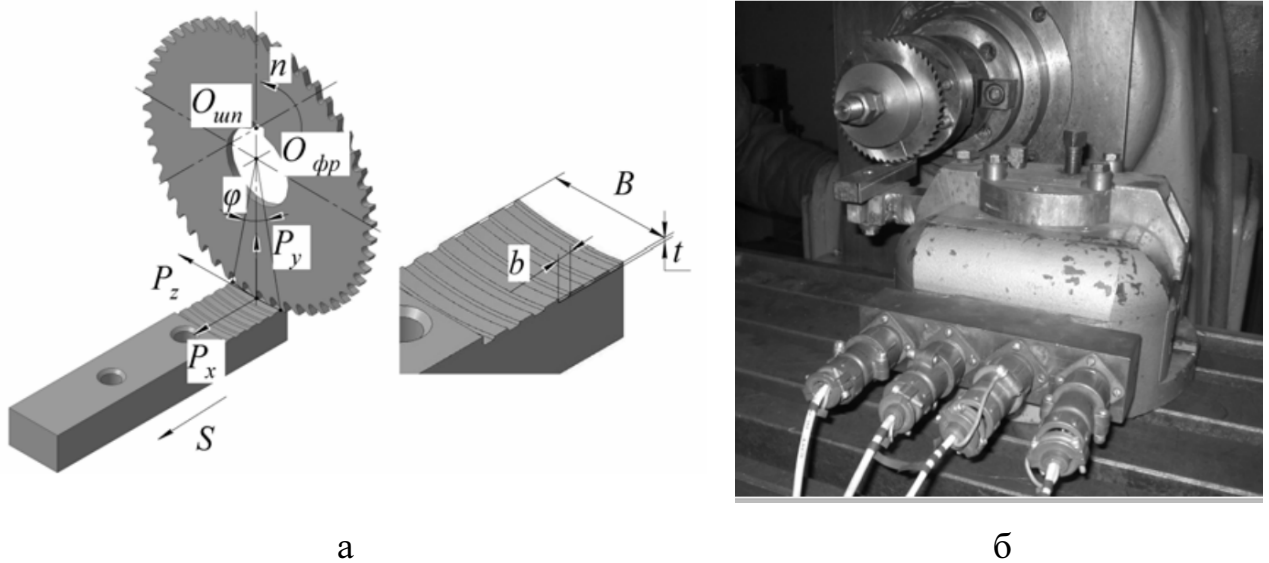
Схема оброблення і установка для вимірювання сили різання імітації контурного фрезерування
